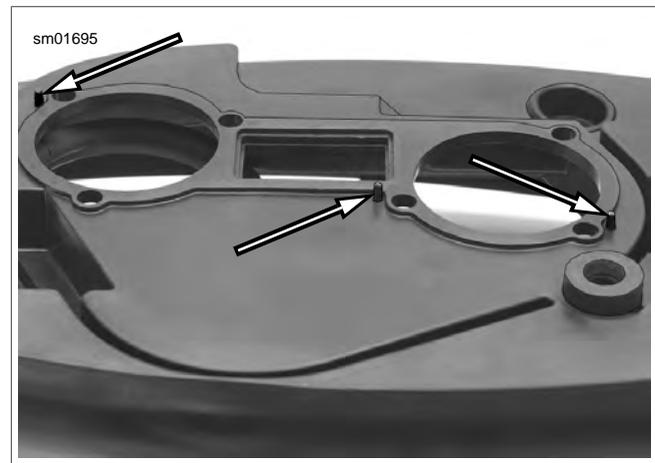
Goupilles d'alignement de joint du filtre à air (3)
